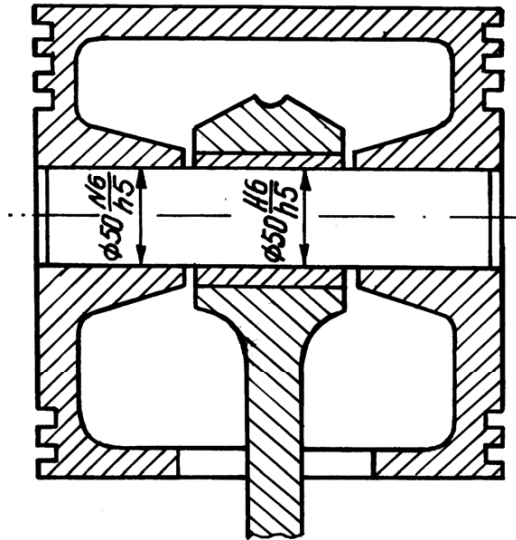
Приклад застосування системи вала для спряжень: втулка верхньої головки шатуна – поршневий палець і бобишка поршня – поршневий палець.
